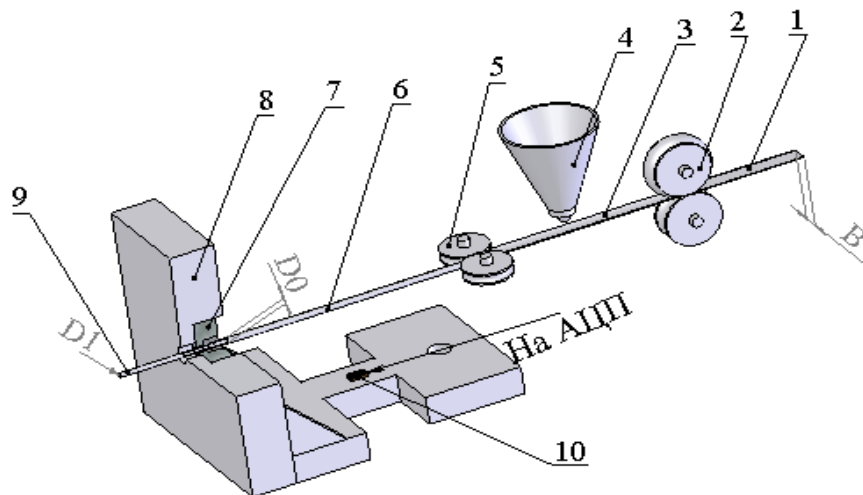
Експериментальна установка: 1 – металева стрічка; 2 - профілеогинальний пристрій; 3 – сформований жолоб; 4 – автоматичний дозатор; 5 - калібруючі ролики; 6 – заготівля порошкового дроту; 7 – фільтр; 8 – волокотримач; 9 – порошковий дріт; 10 – система тензодатчиків для волочіння порошкового дроту
